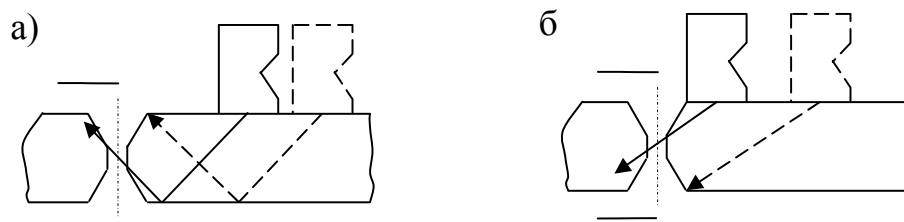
Схемы контроля стыковых сварных соединений
